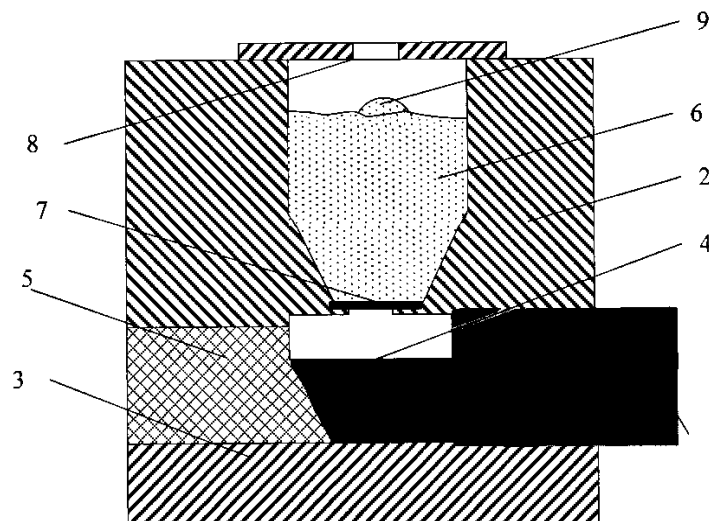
Принципова схема металургійного зварювання: 1 - основа різця; 2 - верхня напівформа; 3 - нижня напівформа; 4 - місце зварювання; 5 - вогнестійкий матеріал; 6 - екзотермічна суміш (у насипному виді); 7 - титанова пластина (товщиною 0,5 мм); 8 - кришка з отвором у центрі для виходу газів; 9 - титановий запал
